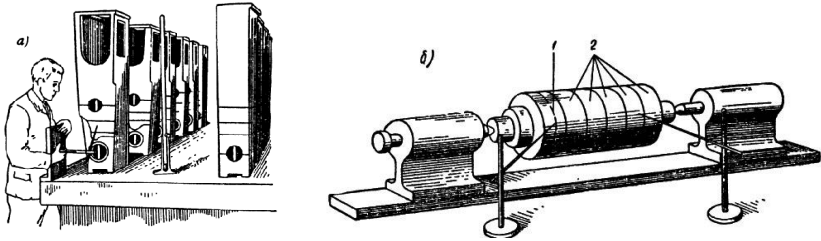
Розмічання партії однакових деталей: а – розмічання партії станин; б – розмічання на оправці в центрах; 1 – еталон; 2 – розмічувані деталі
